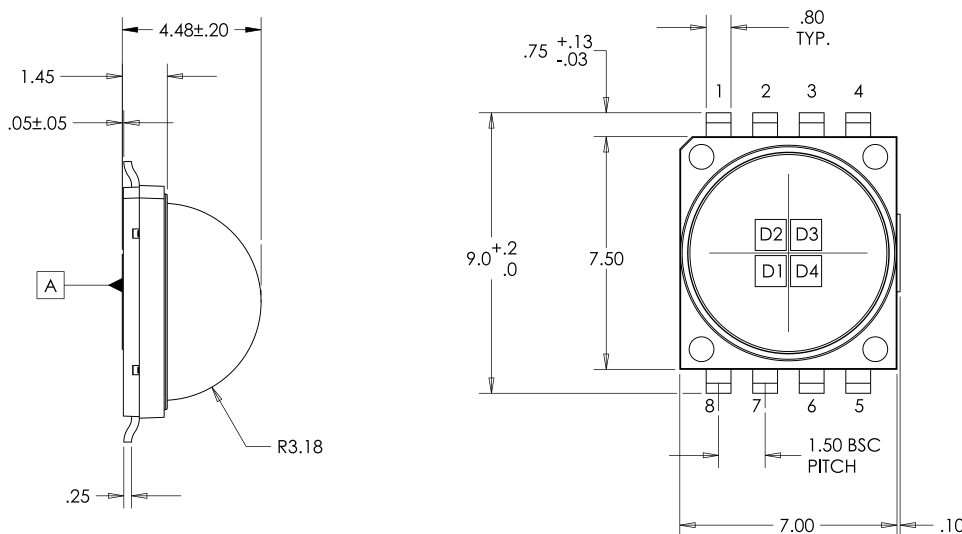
Габаритный чертеж корпуса светодиода серии MC-E
